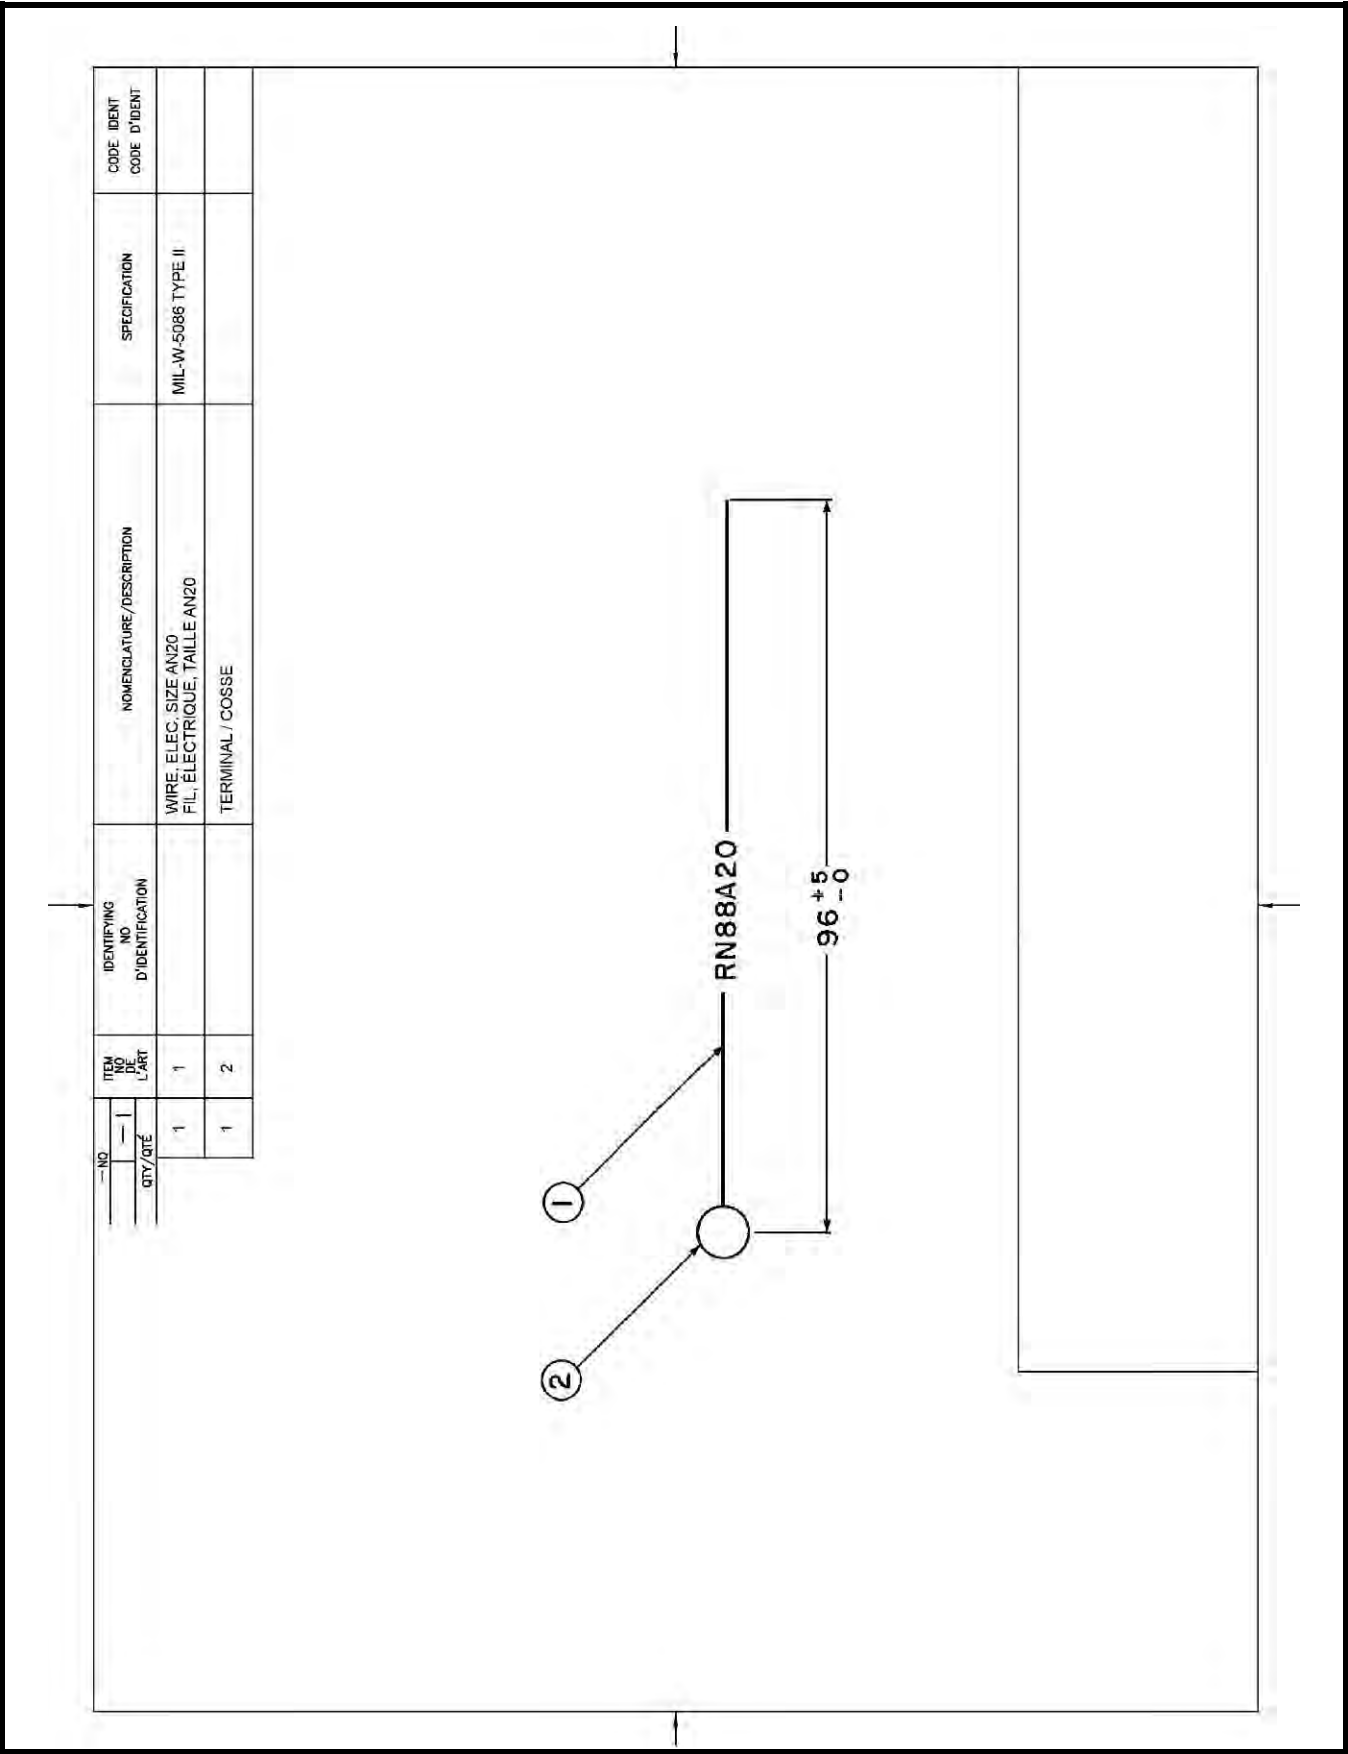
(feuille 1 de 2) Dessin d'ensemble de fil conducteur (conducteur unique)
